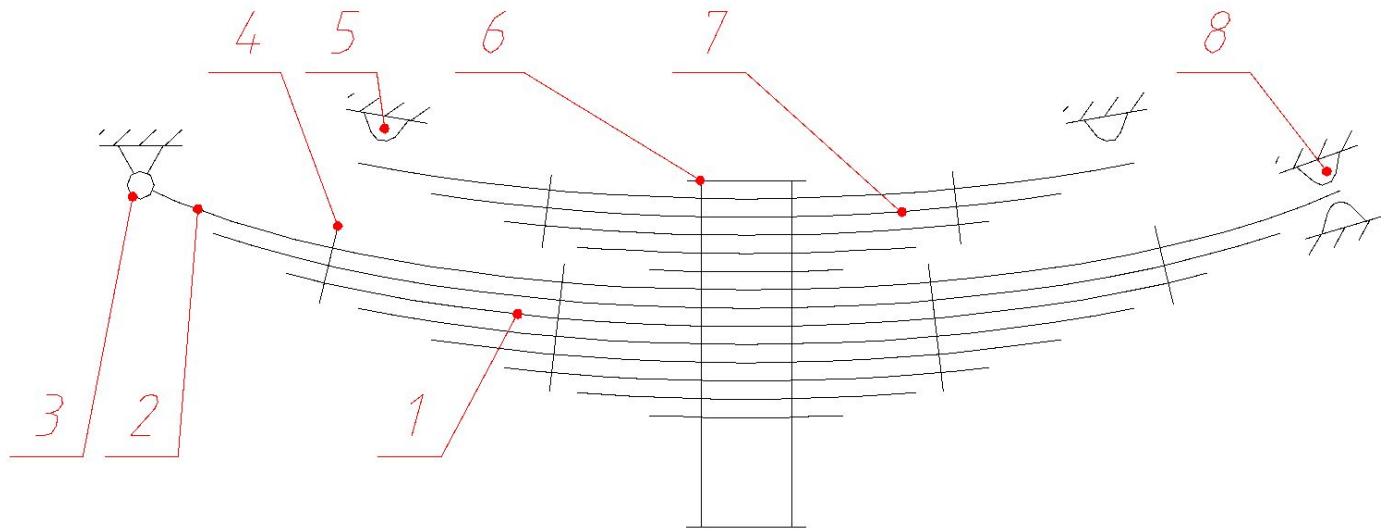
Рессора: 1 – основная рессора, 2 – коренной лист, 3 – передний шарнир, 4 – хомут, 5 – кронштейн дополнительной рессоры, 6 – стремянка, 7 – дополнительная рессора, 8 – задний кронштейн основной рессоры
